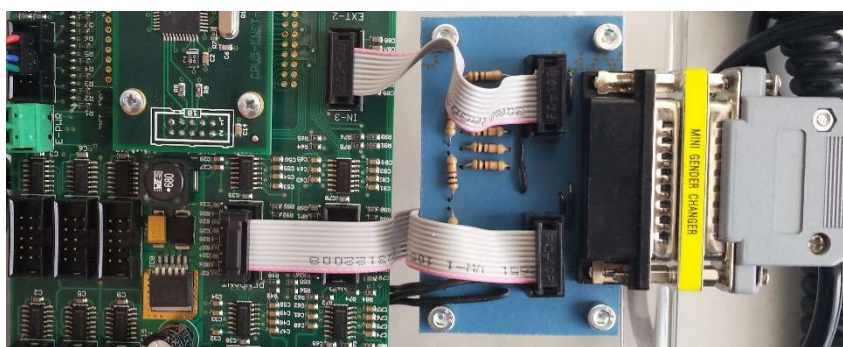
Placa de adaptação do *pendant* montada.
